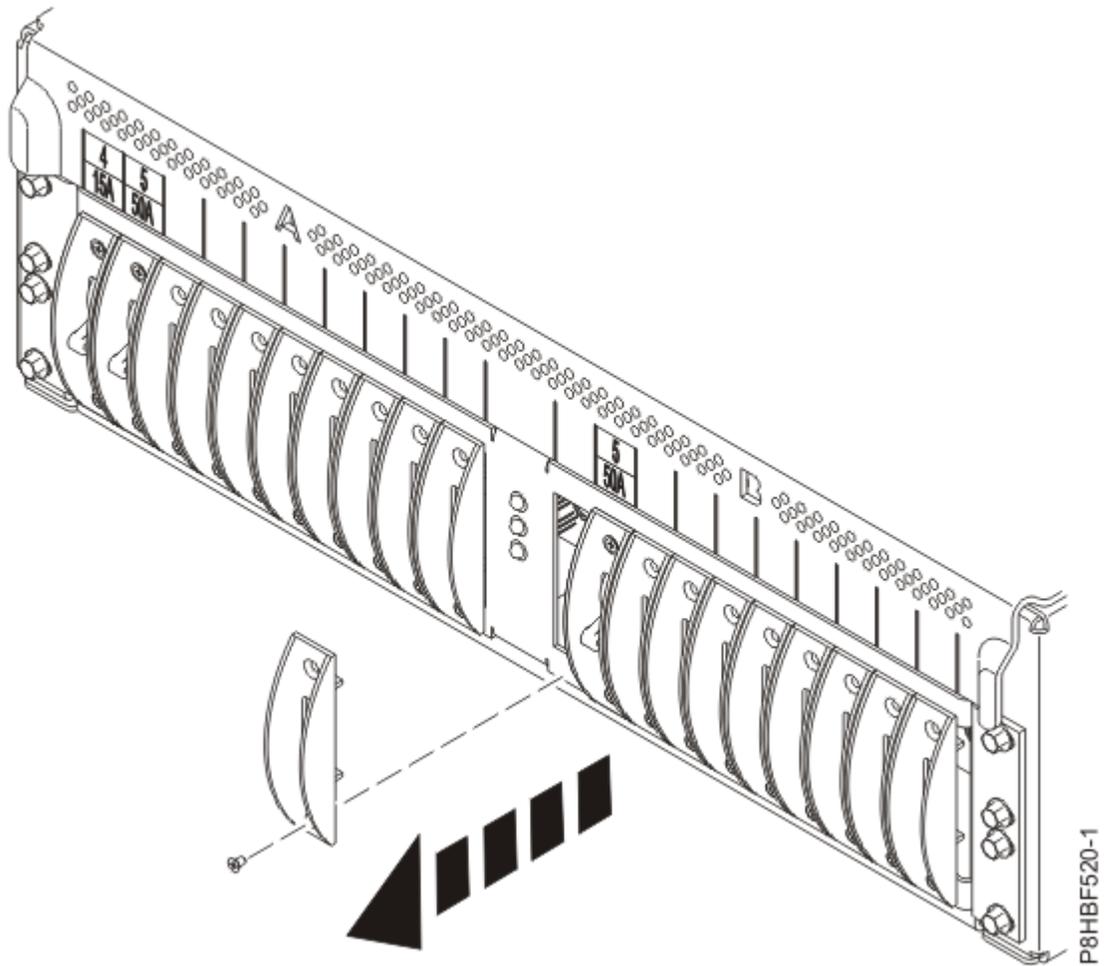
Tampa do disjuntor (a posição do disjuntor mostrado é apenas uma referência)
